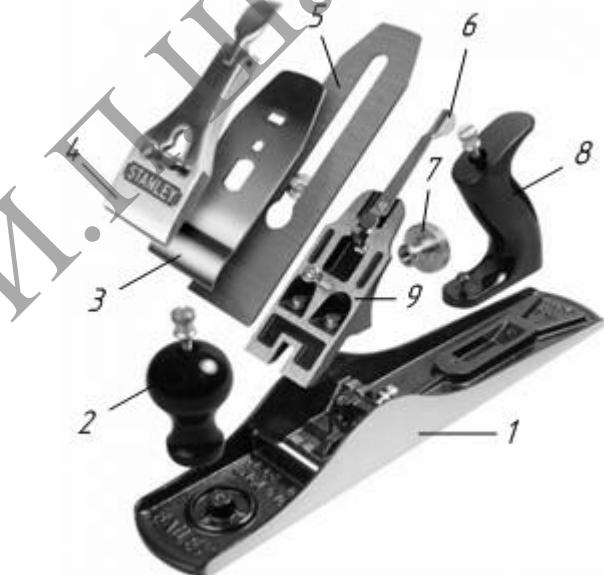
Устройство металлического рубанка с двойным ножом
